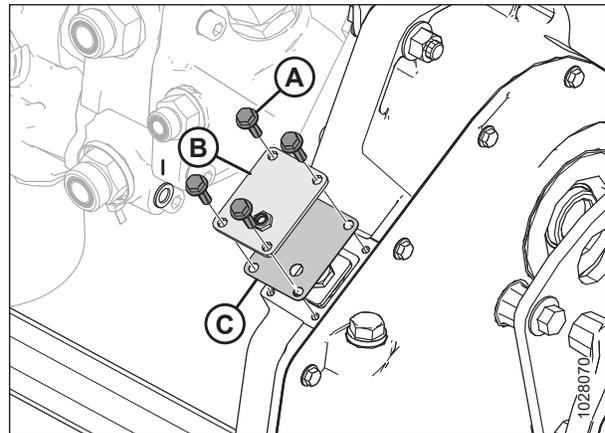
Hauptgetriebe mit Kettenspannerabdeckung
